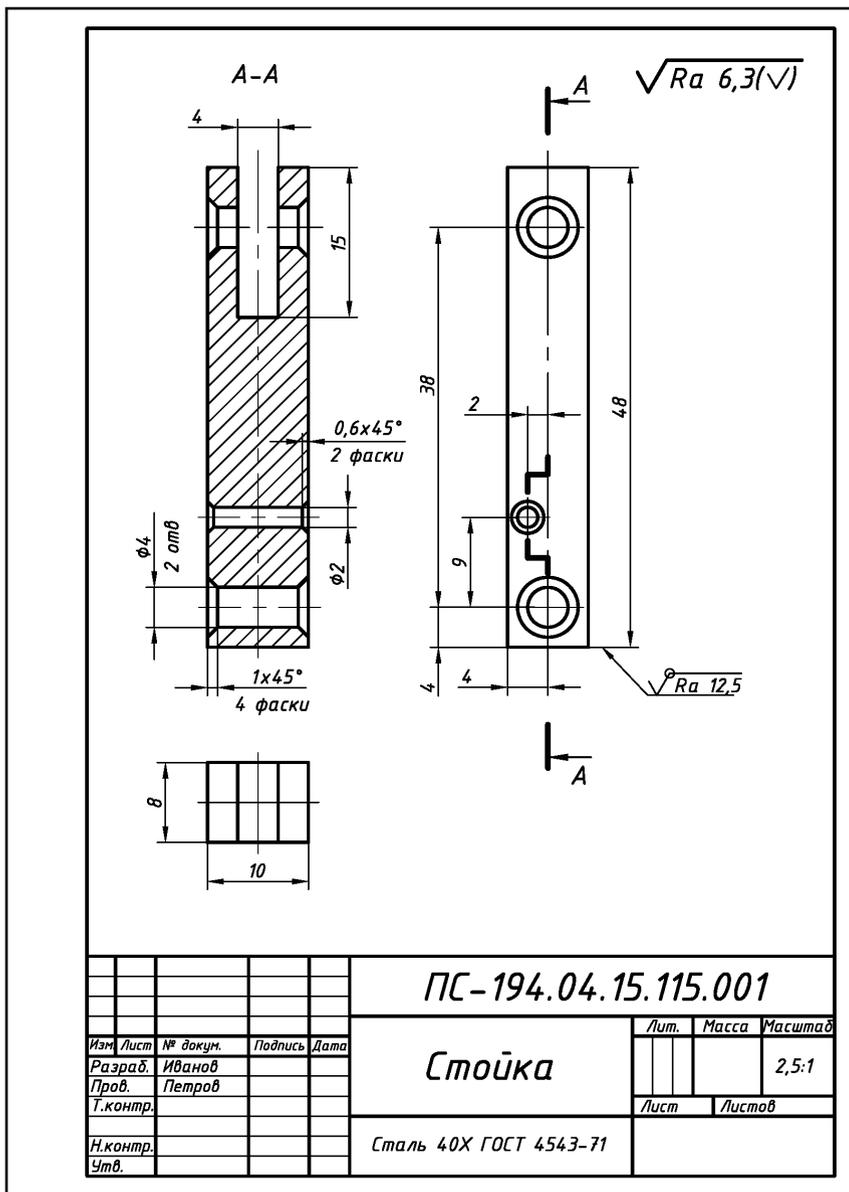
Оформление рабочего чертежа точной детали из металла
